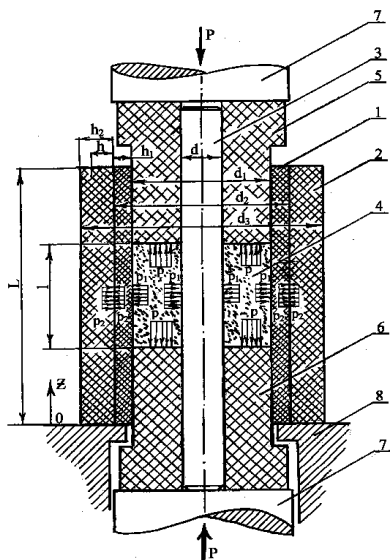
Устройство для прессования изделий из порошков: 1 – вкладыш; 2 – матрица; 3 – центральный стержень; 4 – брикет из порошка; 5, 6 – пуансоны; 7 – поршни пресса; 8 – несущая рама
